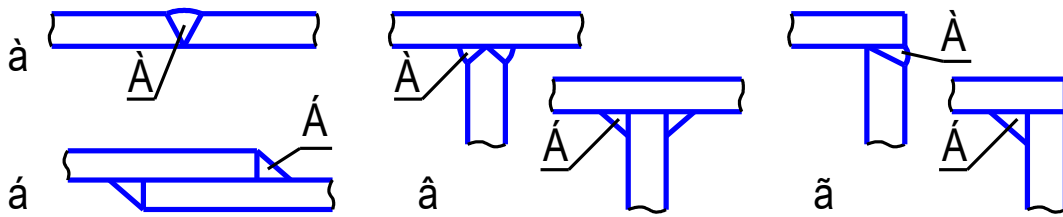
Види зварних з'єднань і типи зварних швів
